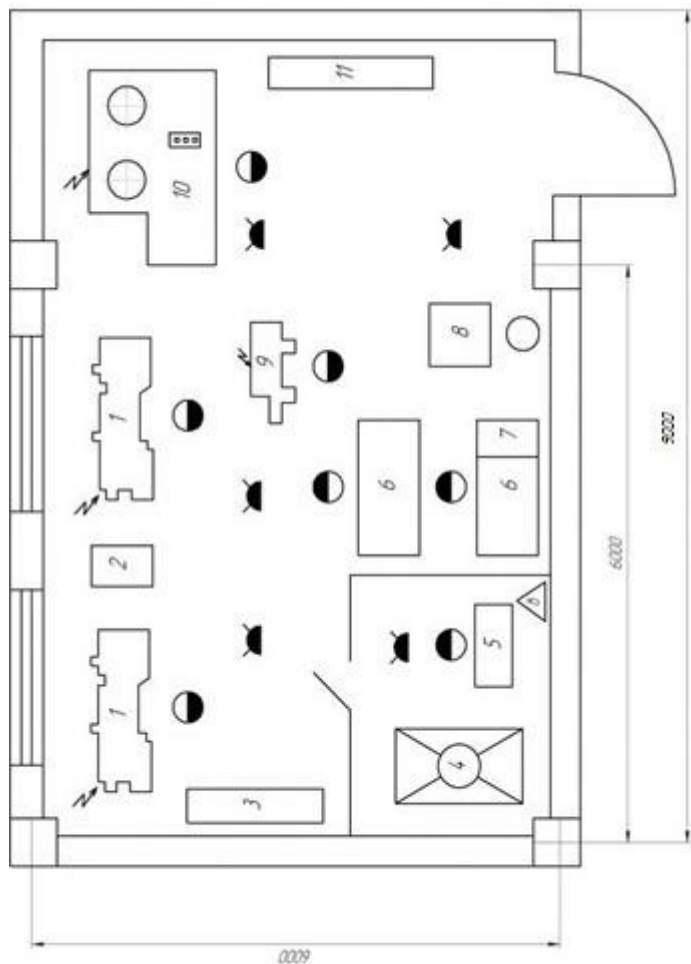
Участок ремонта шестеренных гидронасосов НШ-К с восстановлением и упрочнением деталей: 1-Станок токарно-винторезный; 2-шкаф для инструмента; 3-стеллаж для деталей; 4-выляжная камера; 5-установка ХГДН; 6-верстак на одно рабочее место; 7-установка для электронной обработки; 8-мощная машина; 9-станок универсально-заготовной; 10-стелд контрольно-испытательный; 11-стеллаж для готовой продукции.
